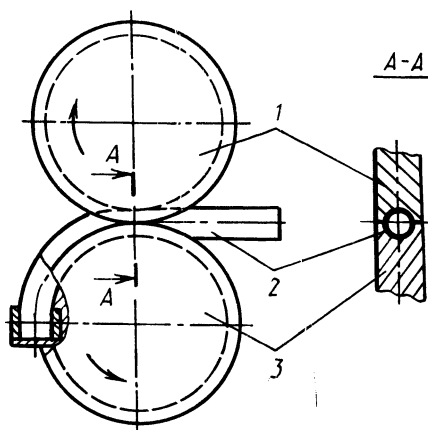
Схема гибки цилиндрической трубчатой заготовки:
